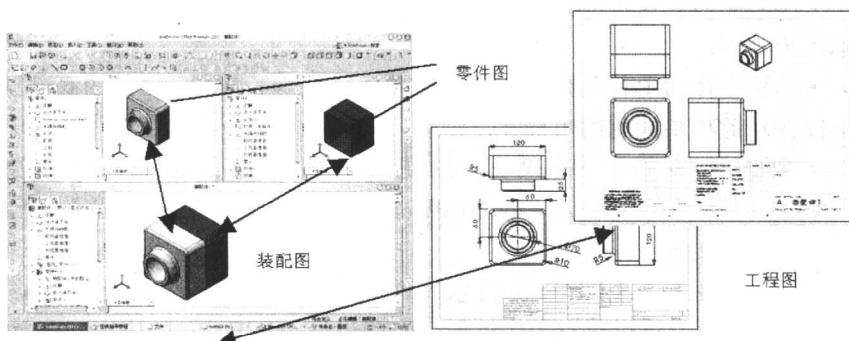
SolidWorks 的三种文件：零件图、装配图、工程图
